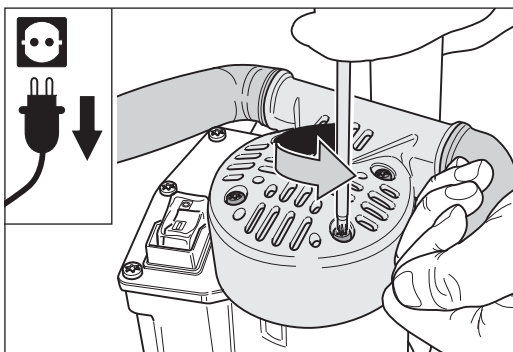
Ta bort handtagets fyra fastsättningskruvar.
